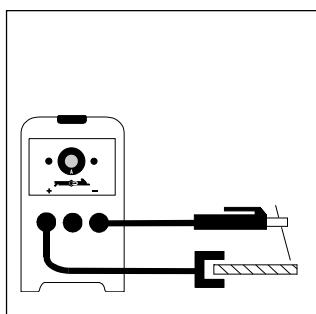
TP 1500 в оснащении для ручной электродной сварки
